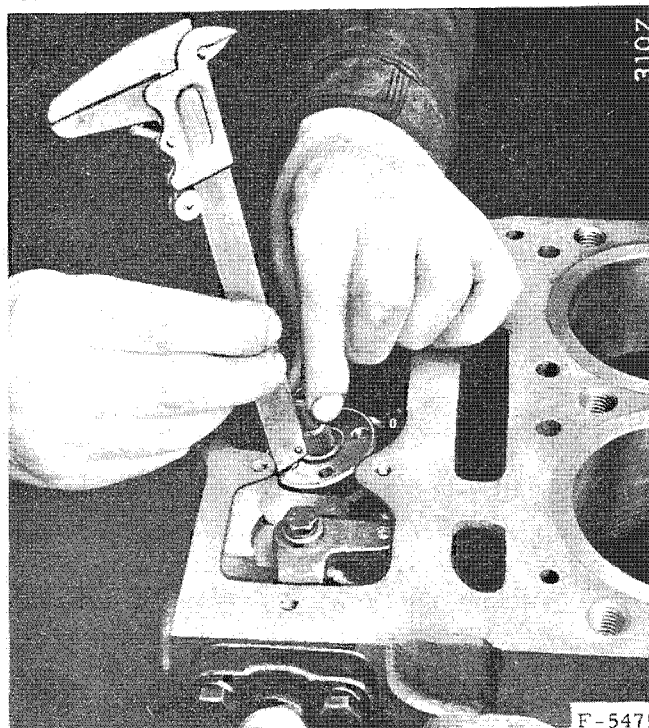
Mesure de la distance D - fig. 1 pour déterminer l'épaisseur des cales à utiliser.
